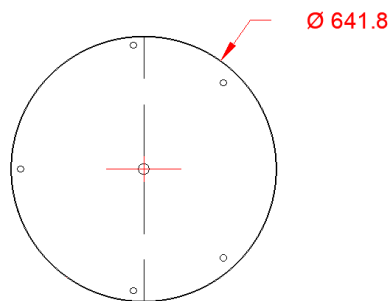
Dimensiones de la tapa de tanque de la marmita [mm].
